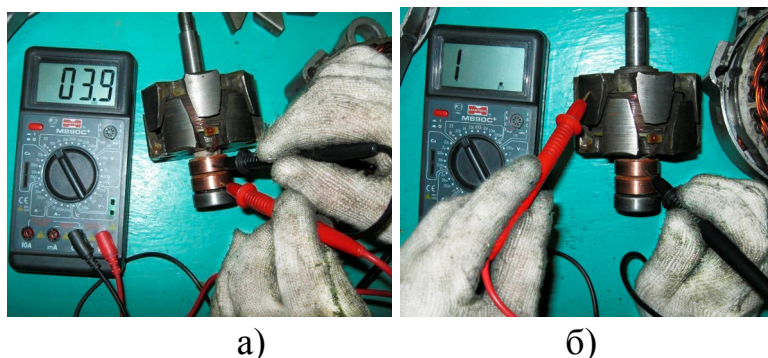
Схема проверки обмотки возбуждения генератора Г-221
